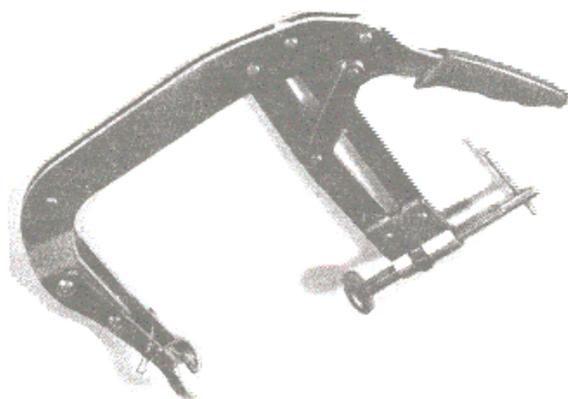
Рычажно-винтовое приспособление для сборки пружин клапанов
